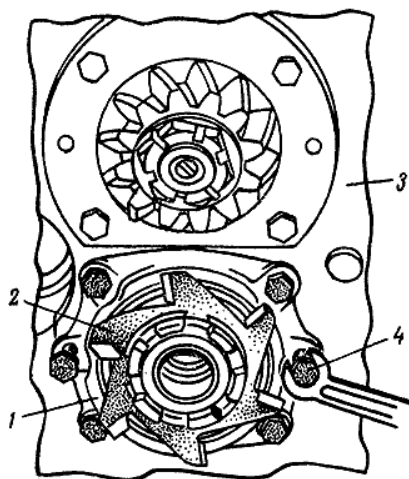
Выпрессовка стакана подшипника ведущей шестерни II ступени редуктора: 1 — стакан; 2 — крыльчатка; 3 — корпус КПП; 4 — технологический болт
